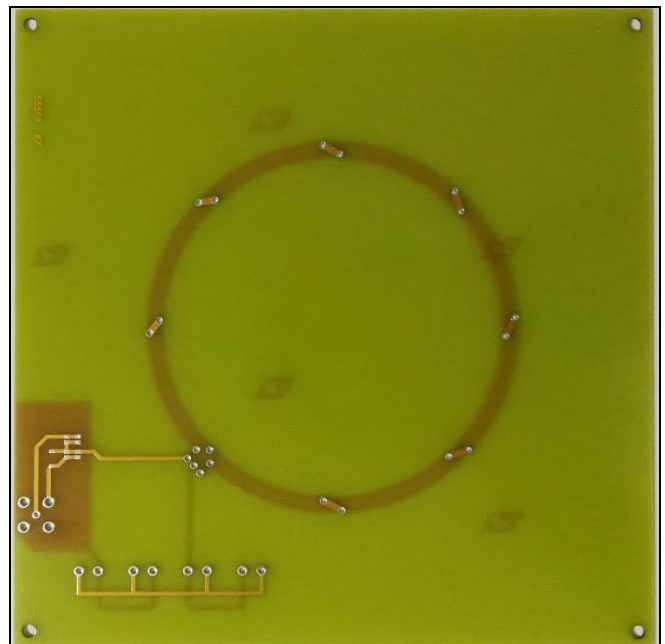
PCB Antena PCD N° 2 incluyendo la red de adaptación de impedancia. BOTTOM
